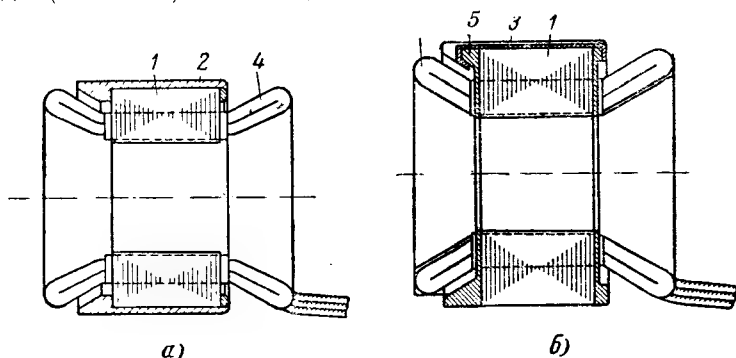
Пакет статора; а — в алюминиевом стакане, б — скрепленный торцовыми шайбами и скобами.
